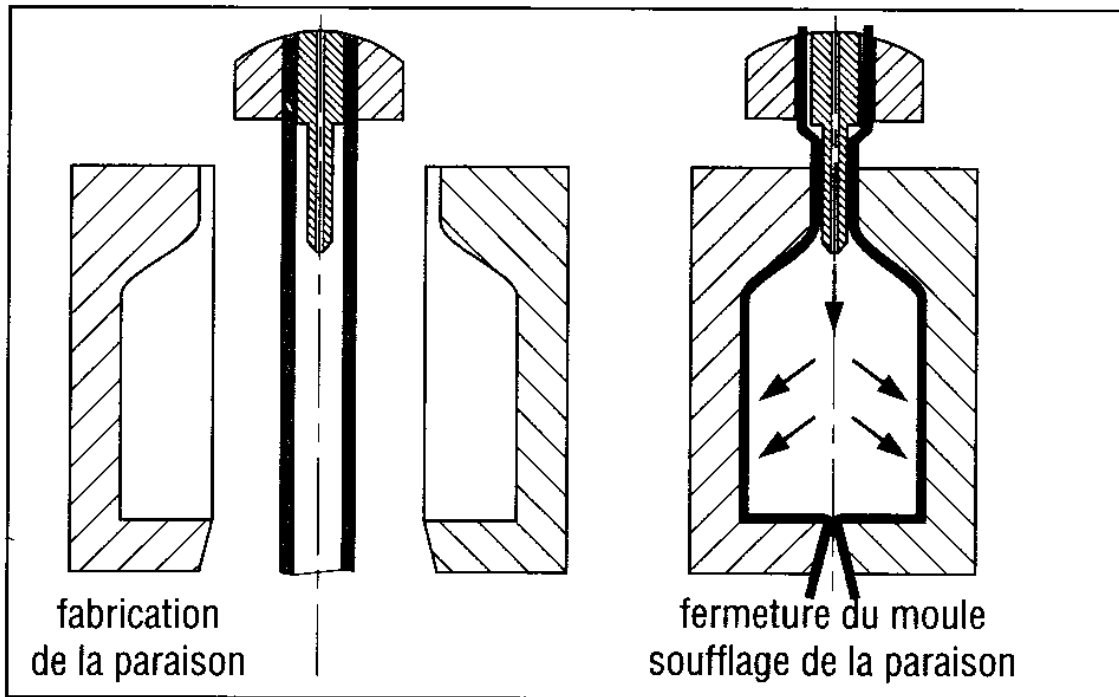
Principe de fabrication d'une bouteille en extrusion-soufflage
